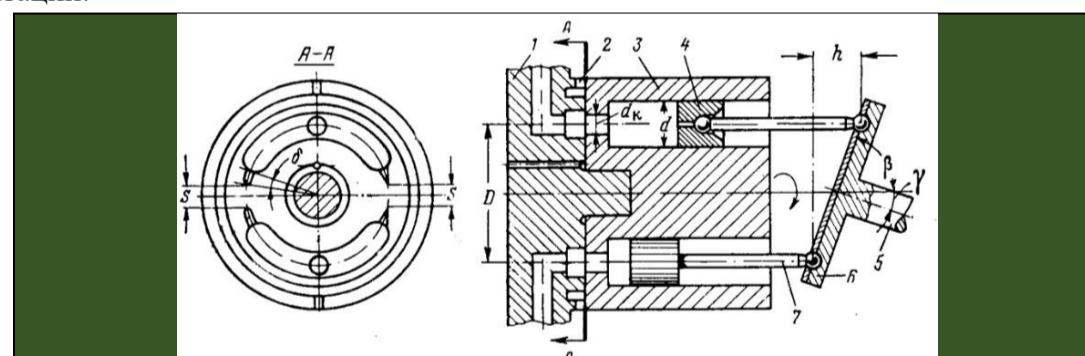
Принципиальная схема аксиально-поршневого насоса: 1-распределительный диск; 2-мост; 3-блок цилиндров; 4-поршень; 5-вал; 6-ведущий диск; 7- шатун
